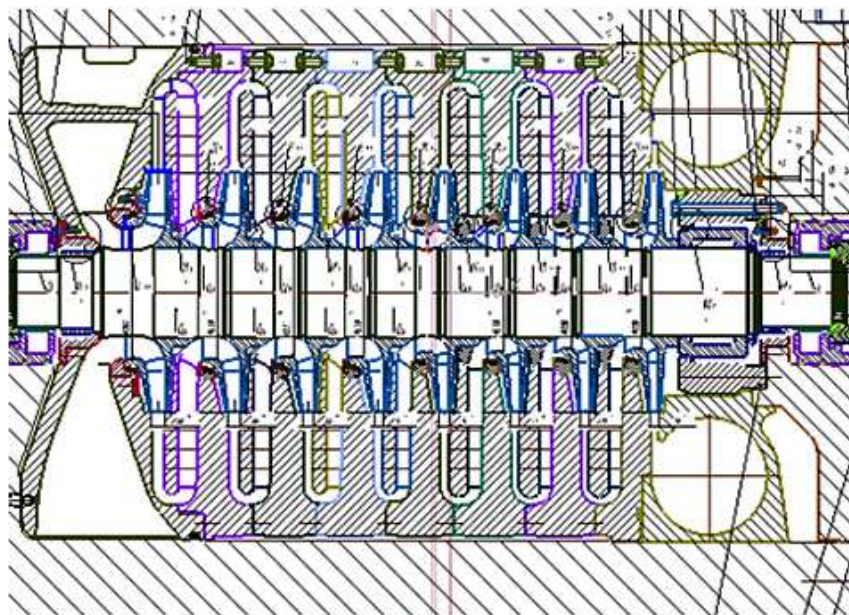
Общий вид конструкции центробежного компрессора ДКС
